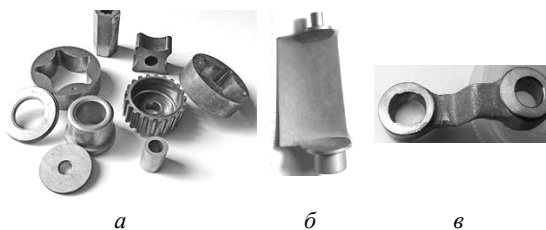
Заготовки, полученные методами порошковой металлургии для различных отраслей промышленности: а – детали машин, б – лопатка направляющего аппарата ГТД; в – рычаг управления положением лопаток направляющего аппарата двигателя ТВ3-117
